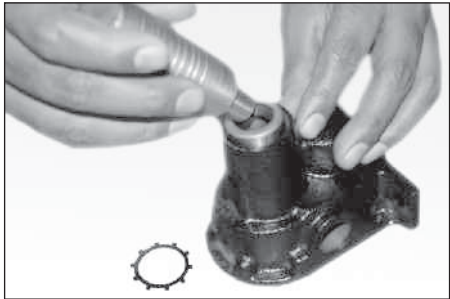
REMPLACEMENT - JOINT À LÈVRE TYPE
